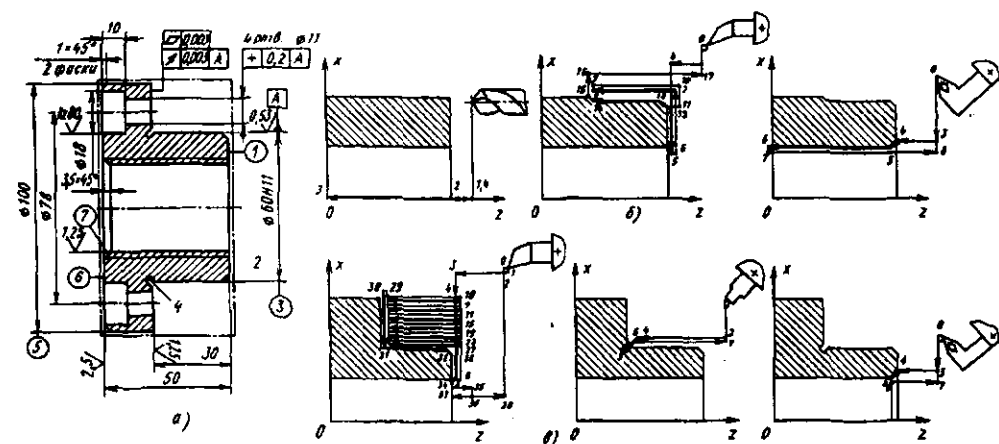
Схемы обработки детали (а) на токарном станке с ЧПУ; б и в – этапы обработки детали
